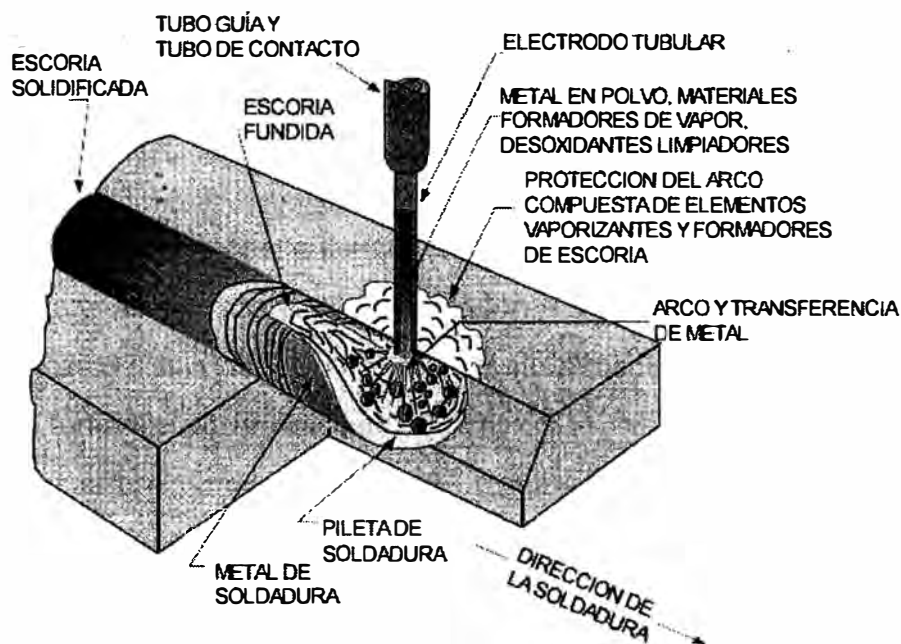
Soldadura por Arco con Alambre Tubular Autoprotegida
